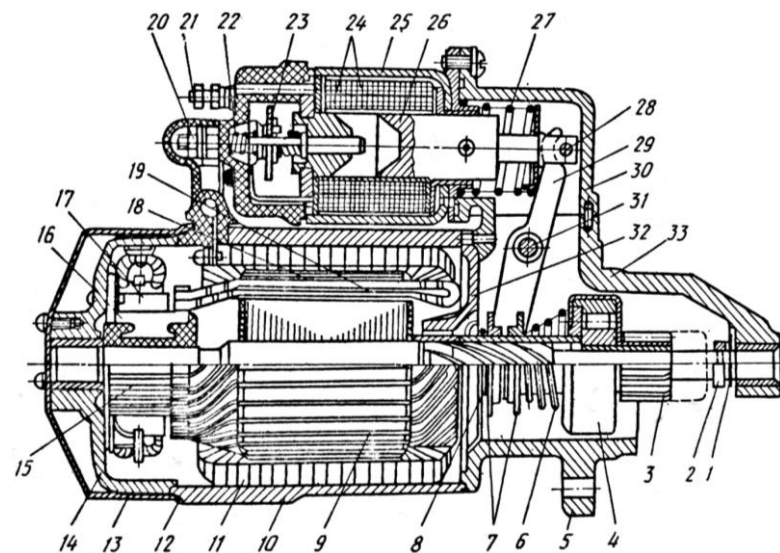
Стартер с цилиндрическим коллектором и роликовой муфтой свободного хода (СТ230):
